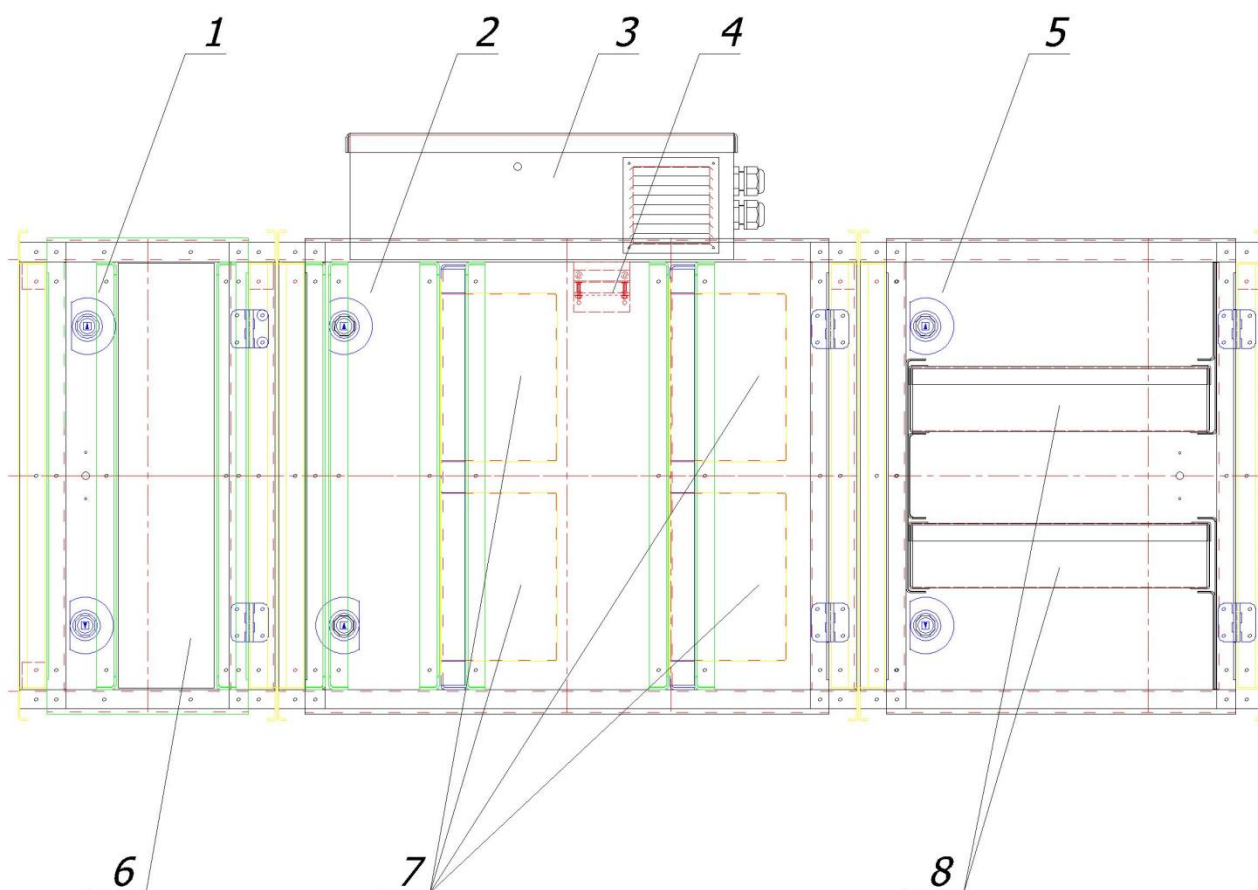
Устройство Газоконвертора "Ятаган "Out"
